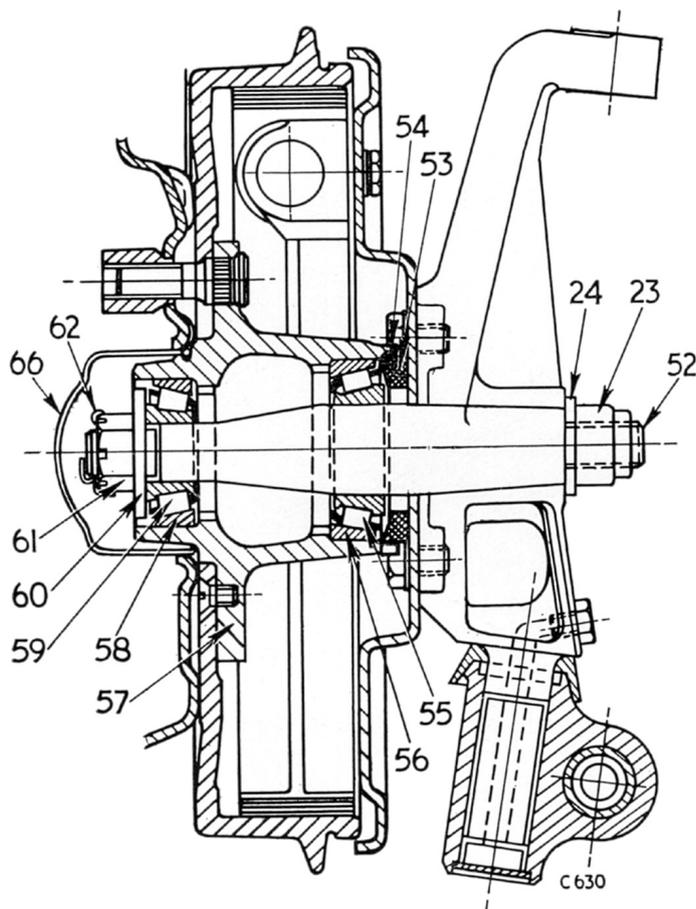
Coupe transversale du frein à tambour et du moyeu sur le modèle Herald 1200
